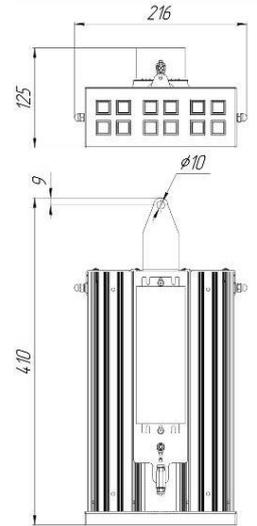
Габаритный чертёж светильника Econex Power 75
